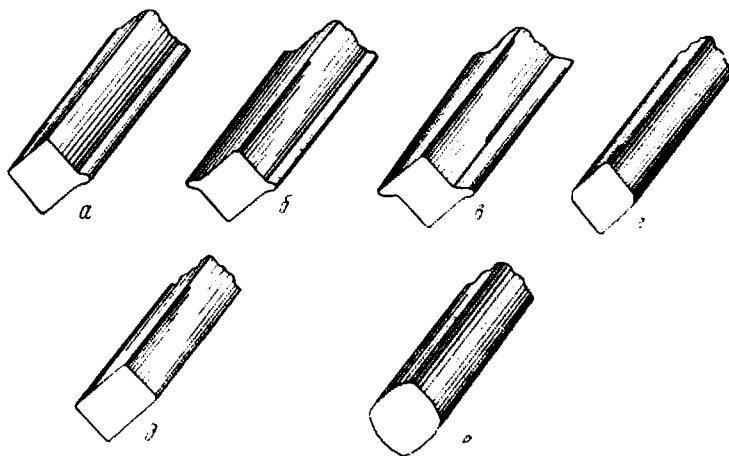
Виды неправильных профилей при прокатке заготовок: а — односторонний лампас; б — двусторонний лампас; в — подрез; г — невыполнение углов заготовки; д — прямоугольное сечение вместо квадратного; е — выпуклые бока
